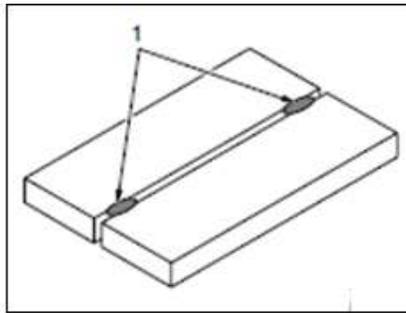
Muestra los dos puntos de soldadura
